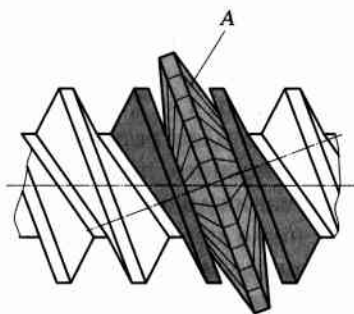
Схема нарезания червяка дисковой фрезой
